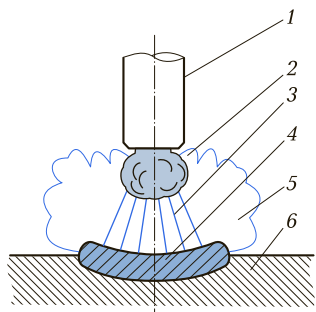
Схема электрической сварочной дуги:
